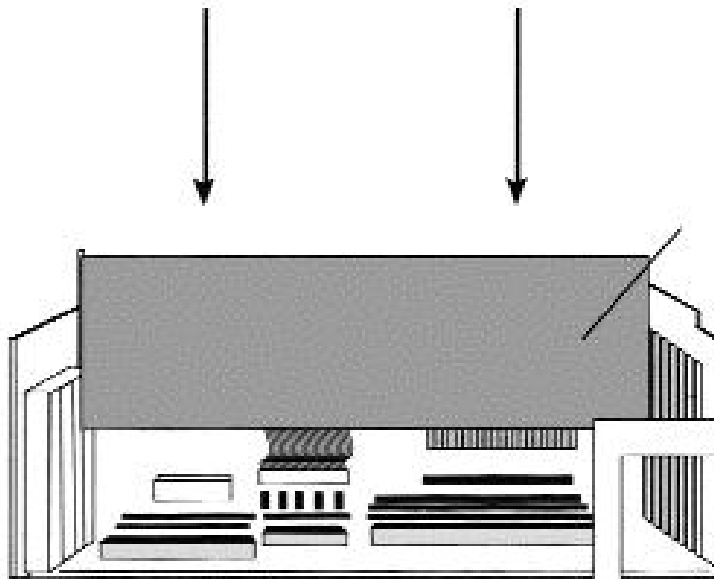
Einsetzen des BLIZZARD 2060 Turbo Boards
